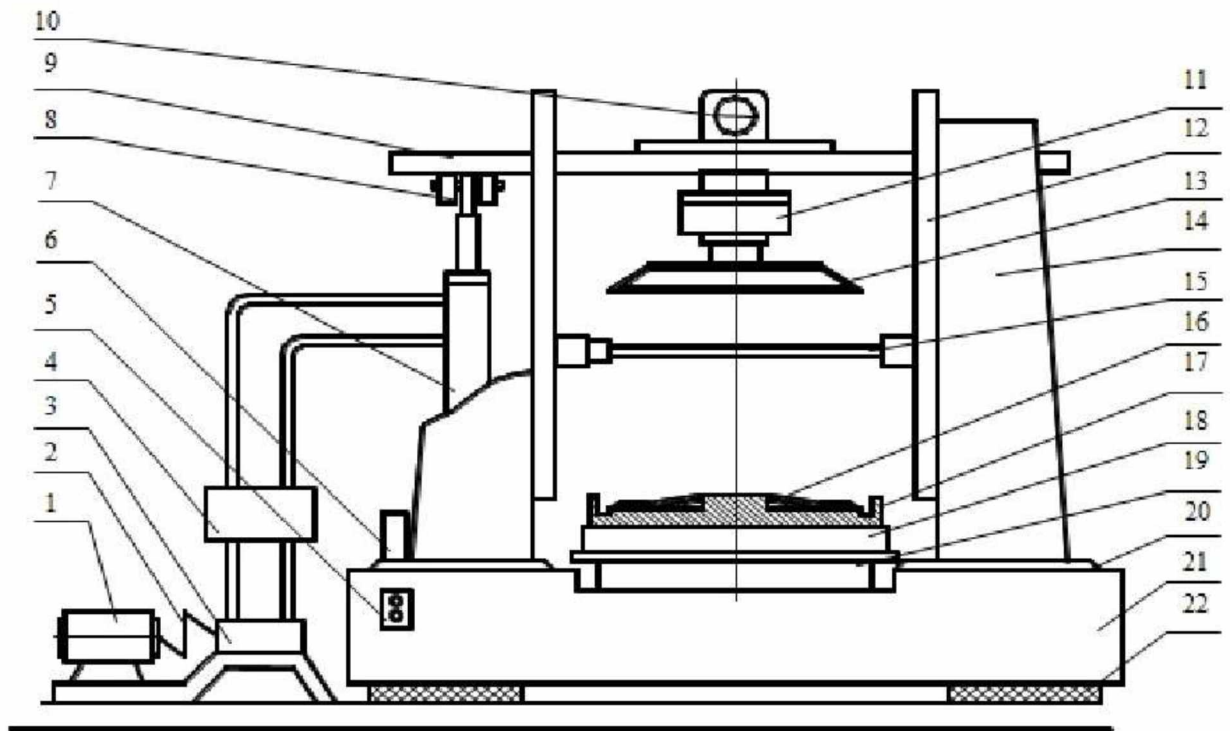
Схема установки: 1 – електродвигун; 2 – муфта; 3 – гідронасос; 4 – розподільник; 5 – пускач; 6 – бак; 7 – гідроциліндр; 8 – гумові амортизатори; 9 – плита вібратора; 10 – вібратор; 11 – затисне устаткування; 12 – направляюча; 13 – робочий інструмент; 14 – стійка; 15 – стяжка; 16 – матриця; 17 – деталь; 18 – основа; 19 – плита; 20 – опорна плита; 21 – брус; 22 – амортизатор
